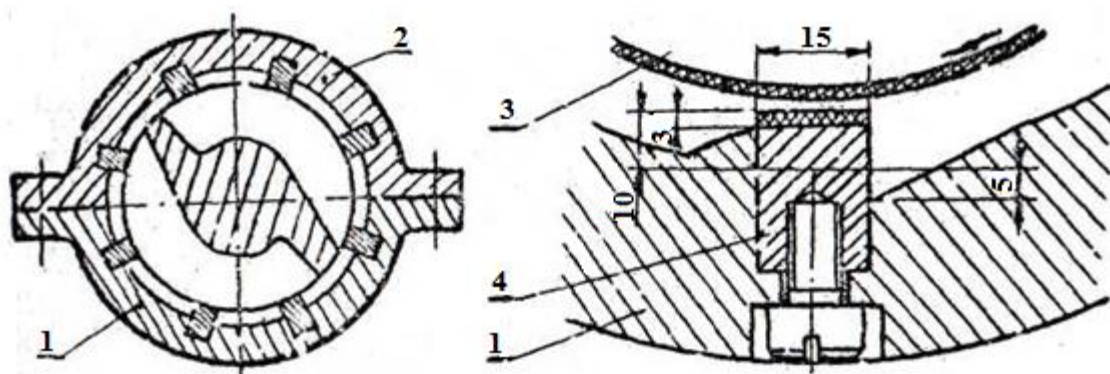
Поперечный разрез конической части шнекового питателя: 1-нижняя половина корпуса питателя; 2-верхняя половина корпуса питателя; 3-шнек; 4-продольный нож
